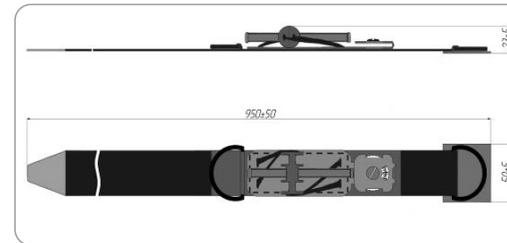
Внешний вид и габаритные размеры ЖК-01
